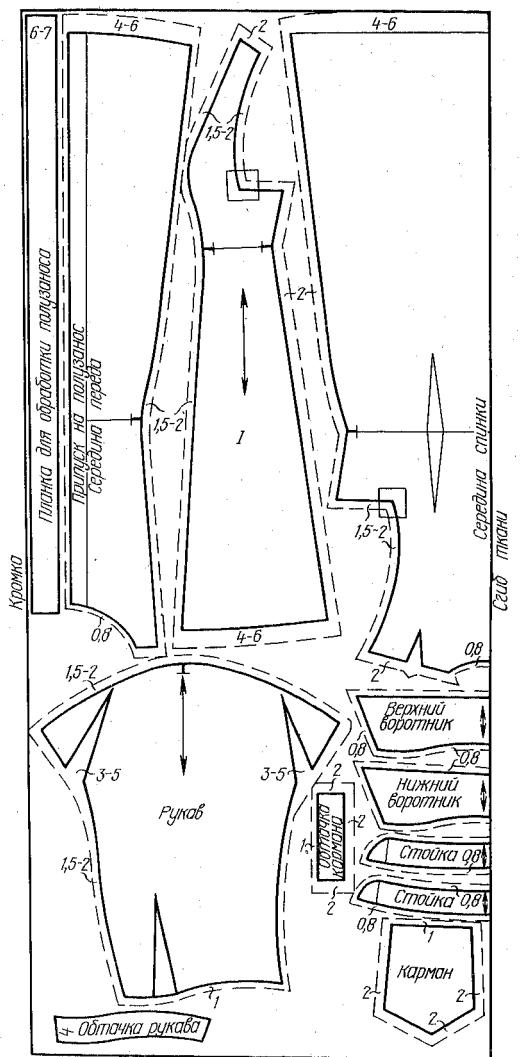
Раскладка выкроек на ткани и раскрой платья с квадратной проймой и застежкой посередине переда
